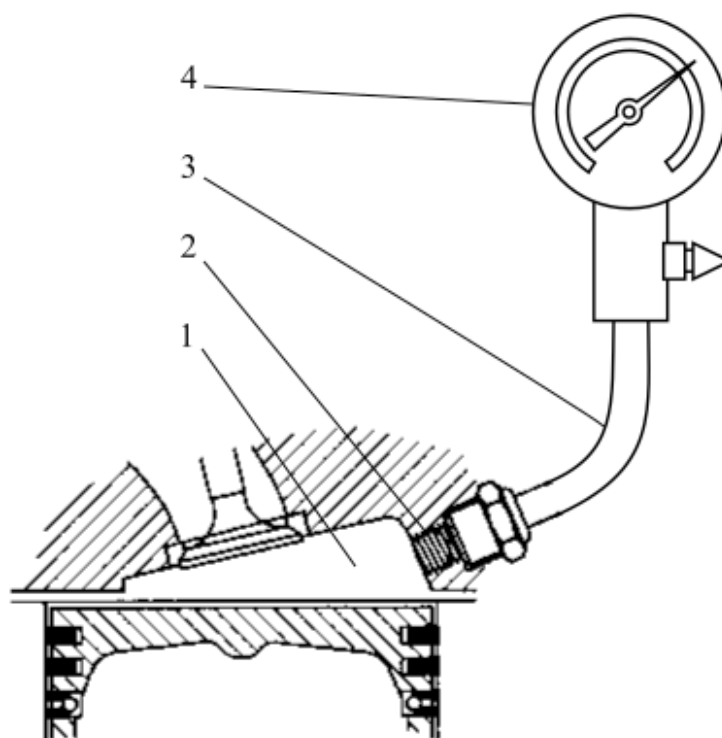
Схема замера компрессии двигателя с искровым зажиганием: 1 — камера сгорания, 2 — резьбовое отверстие для установки свечи, 3 — присоединительный шланг, 4 — манометр
